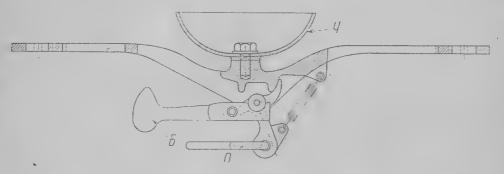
Сигнальный звонок кондуктора: U — чашка звонка, B — боек, O — отверстве для веревки.
